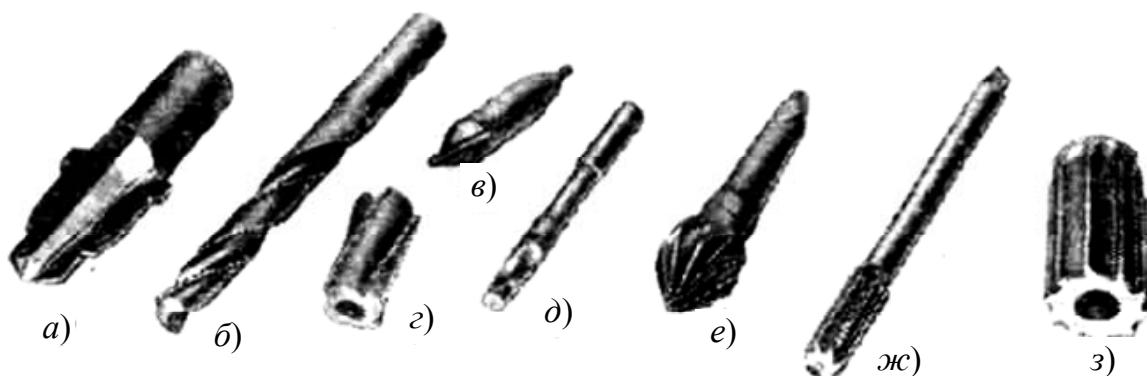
Фотографии осевых инструментов: комбинированного (а); винтового сверла (б); комбинированного центровочного сверла (в); насадной головки зенкера (г); зенкера (д); зенковки (е); развертки (ж); насадной головки развертки (з)
